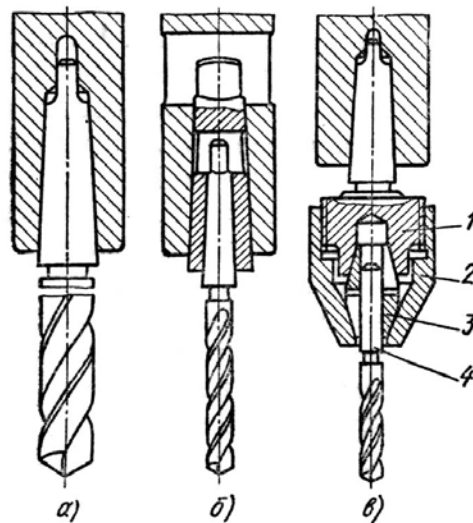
Закрепление инструмента на сверлильных станках:
